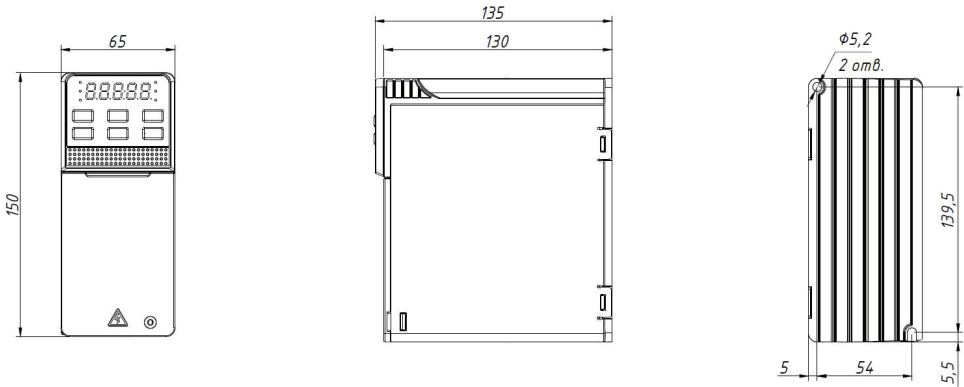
Чертеж преобразователя частоты типоразмера С1
